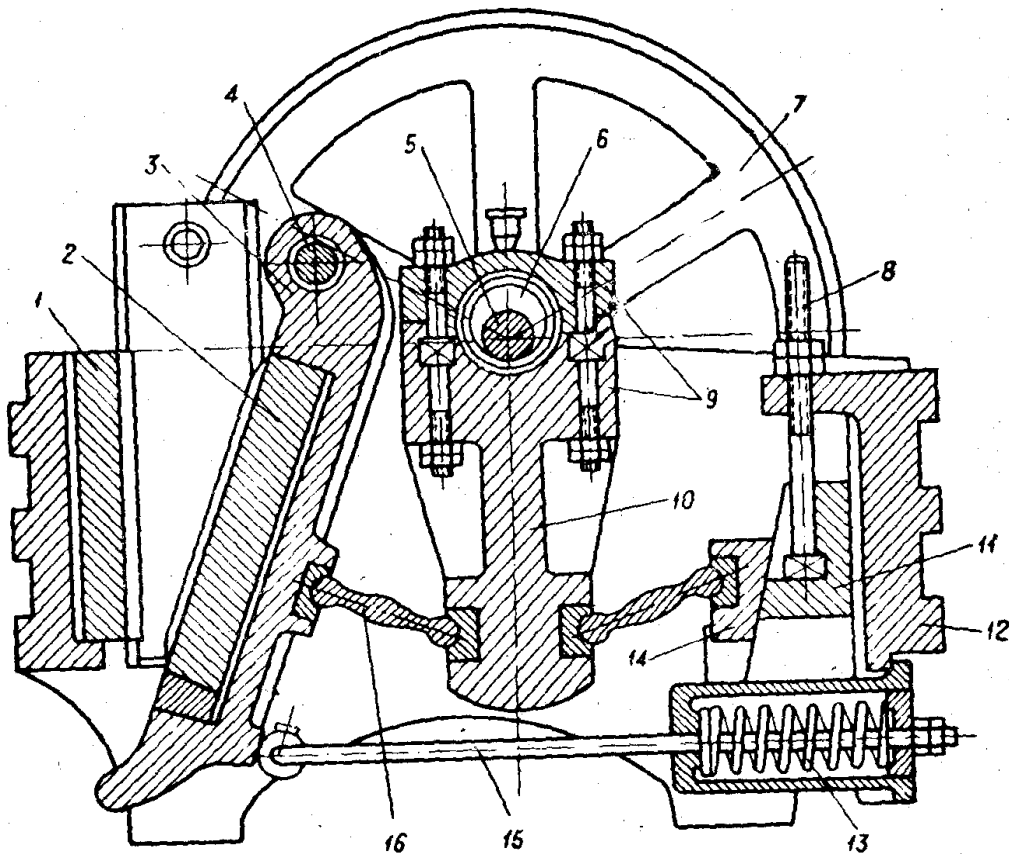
Щековая дробилка, с простым движением щеки: 1 – неподвижная щека; 2 – съемная плита; 3 – подвижная щека; 4 – ось; 5 – вал; 6 – эксцентрик; 7 – маховое колесо; 8 – винт; 9 – подшипники; 10 – шатун; 11 – подвижный ползун; 12 – станина; 13 – пружина; 14 – ползун; 15 – тяга; 16 – распорная плита
